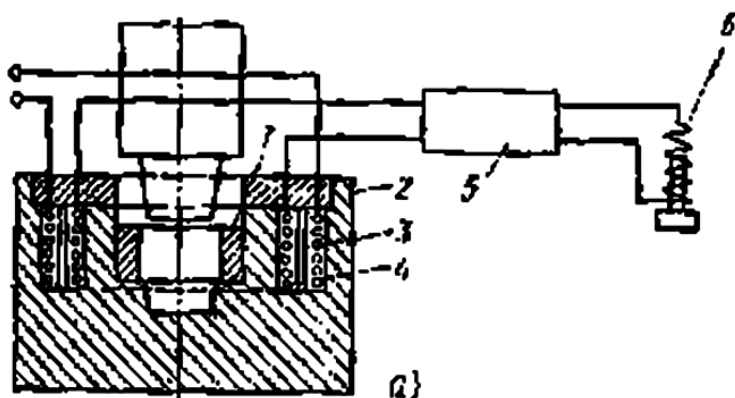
Схема штампа для штамповки в условиях сверхпластичности: 1 – заготовка; 2 – матрица; 3 – коаксиальная обмотка; 4 – коаксиальная обмотка; 5 – усилитель; 6 – электромагнитное реле.
